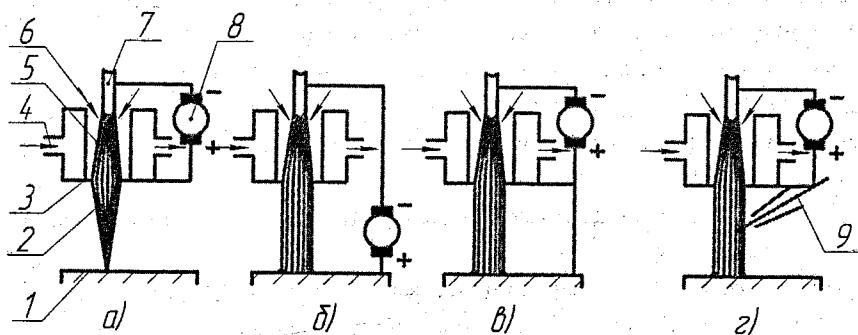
Можливі схеми ведення плазмового наплавлення і різання металу:
